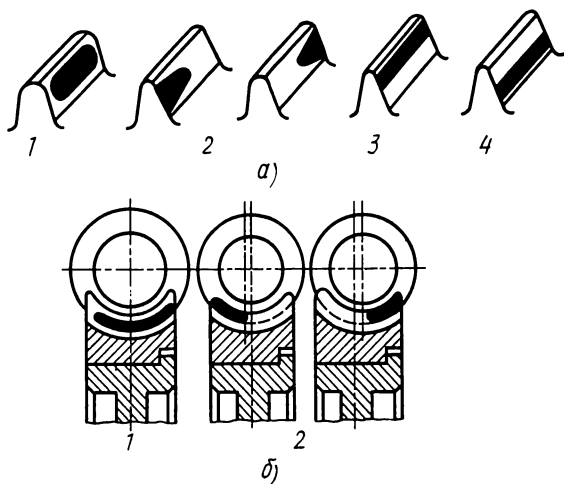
Форма и расположение пятен контакта на поверхности зубьев колес:
